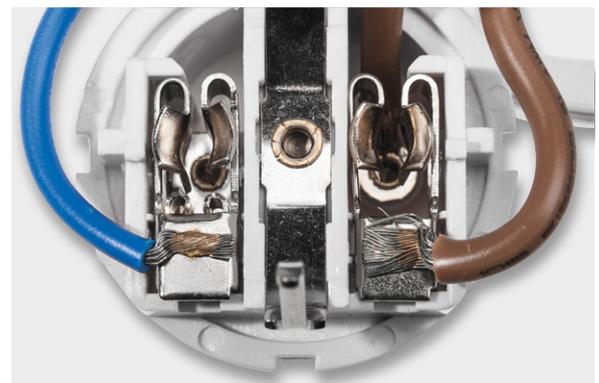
Schlampig verschweißt: die Kabelanschlüsse an der Netzsteckereinheit
